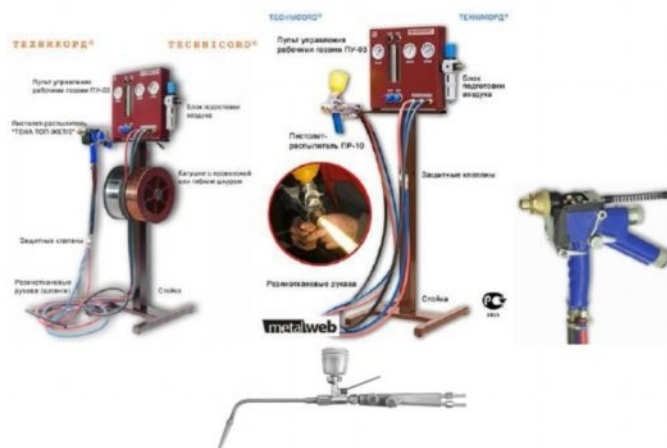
Оборудование для газопламенного напыления и газопорошковой наплавки защитных покрытий
